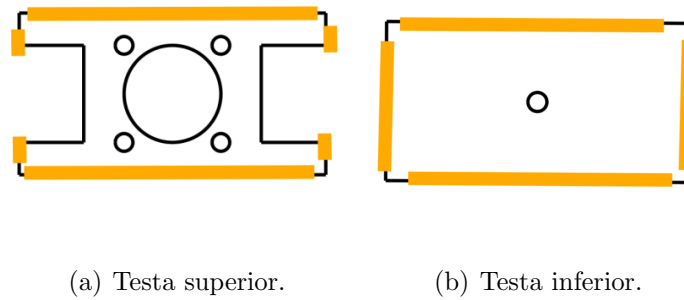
Cordones de soldadura empleados en las testas.
